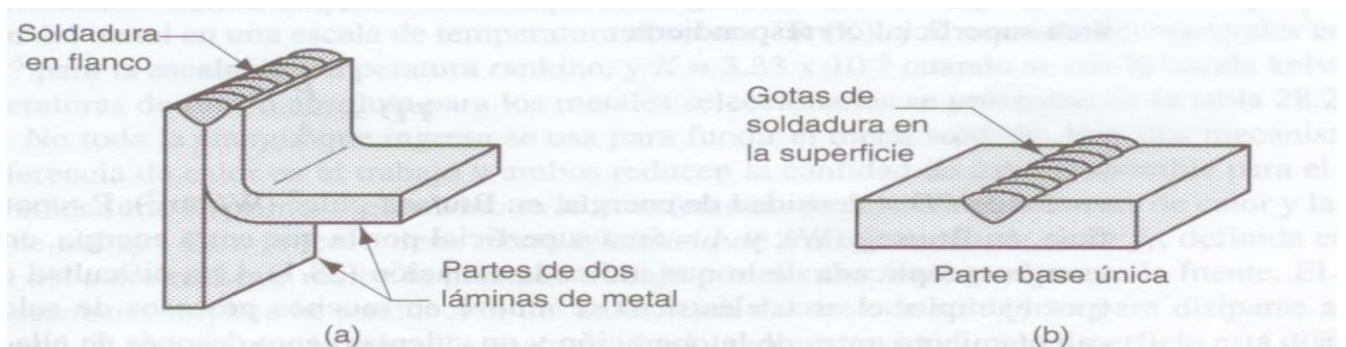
(a) Soldadura en flanco y (b) soldadura en superficie.
